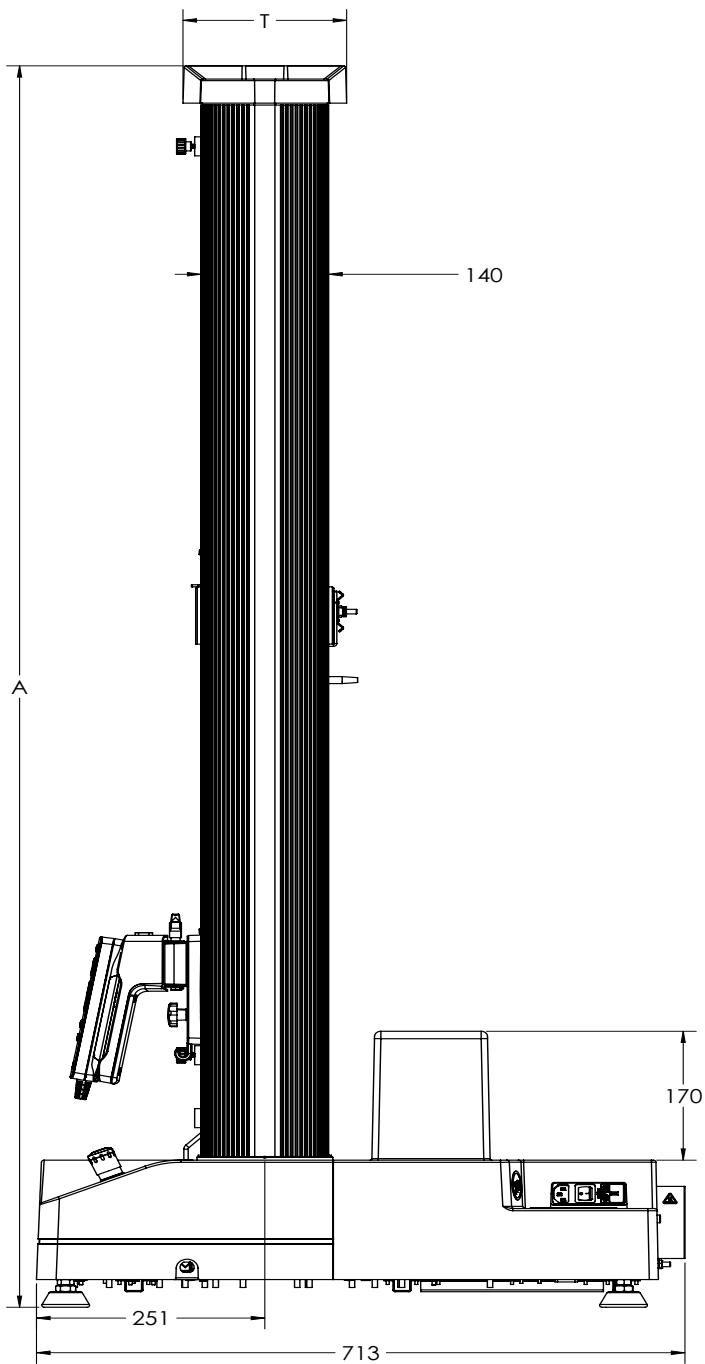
68TM-30 Dimensions du bâti - vue latérale
